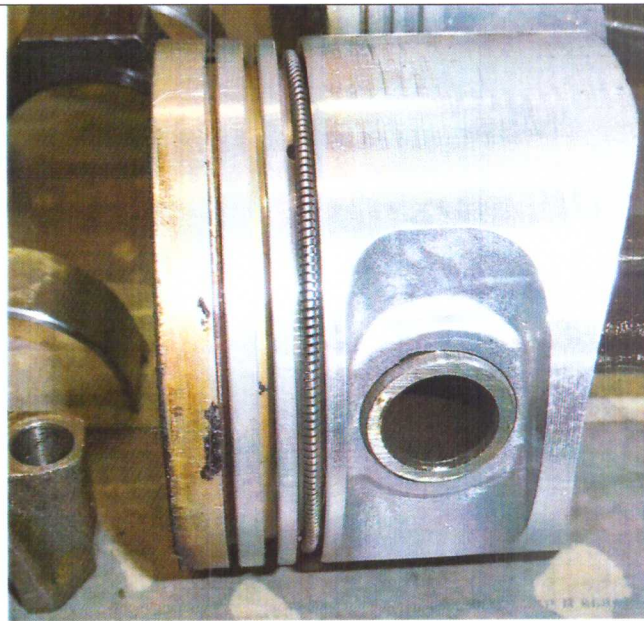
Внешний вид боковой поверхности поршня четвертого цилиндра по окончании длительных испытаний двигателя при работе на базовом масле Castrol EDGE
